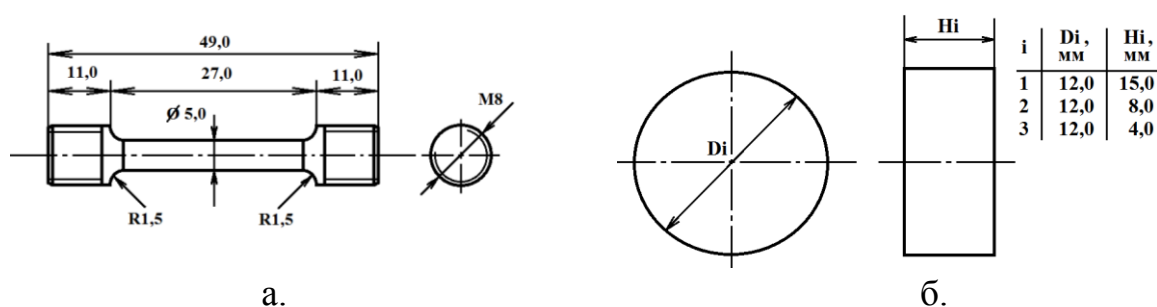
Образцы для горячих испытаний в условиях простого нагружения: а- образец для одноосного растяжения; б- образец для одноосного сжатия.
